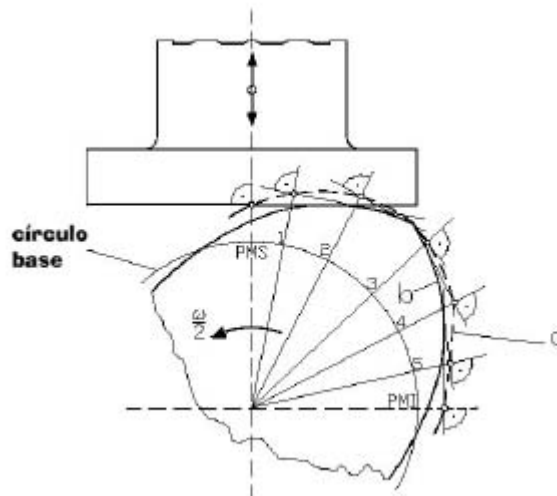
Construcción de la forma de una leva para empujador plano
